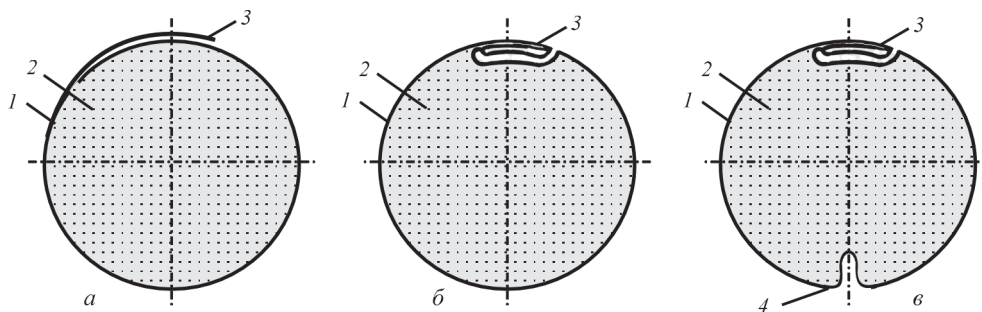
Виды соединения порошковой проволоки: а — внахлест; б, в — с замковым соединением (1 — оболочка; 2 — наполнитель; 3 — замок; 4 — компенсатор)
